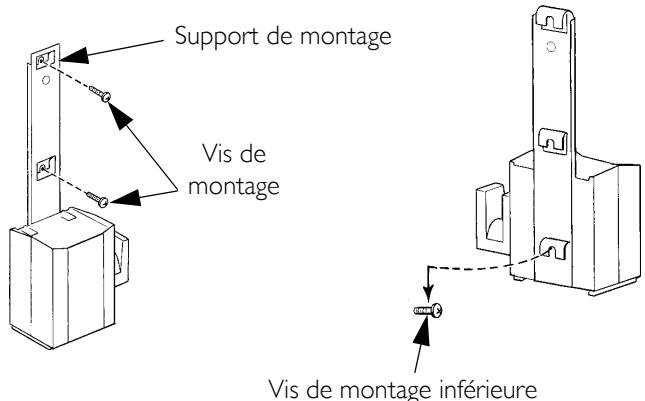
Fixation au mur du support de montage du chargeur de la batterie
